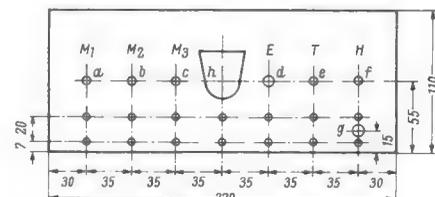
Frontplatte aus 2-mm-Tiefziehblech; a bis f = Bohrungen für Potentiometer und Schalter, g = Bohrung für Netzschalter, h = Ausschnitt für Anzeigeröhre. Die beiden Lochreihen im unteren Teil der Platte sind zusammen mit dem Chassis zu bohren, Lochdurchmesser 3 mm für Senknieten, oder 3,2 mm für M-3-Senkschrauben; Chassis und Frontplatte sind hiermit aneinander zu befestigen
